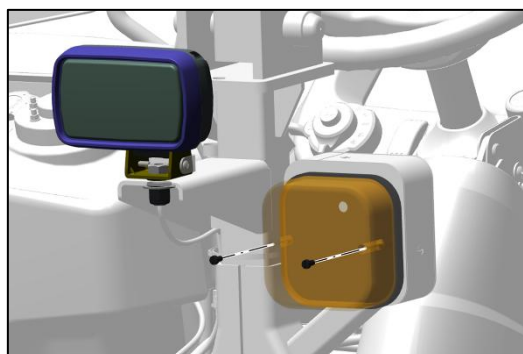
WECHSELN DER GLÜHLAMPE DES HINTEREN BLINKERS
